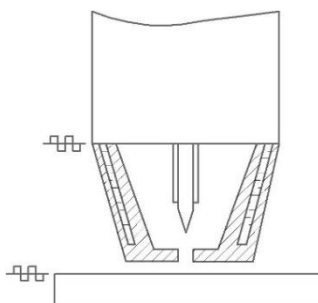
Схема плазменной сварки разнополярными прямоугольными импульсами тока
